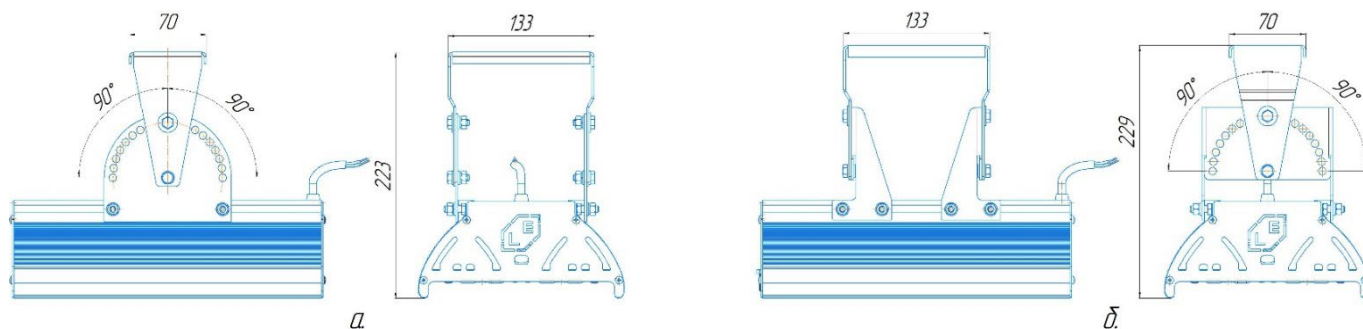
Светильник с кронштейнами продольного (а) и поперечного (б) поворота (доп. опции)
